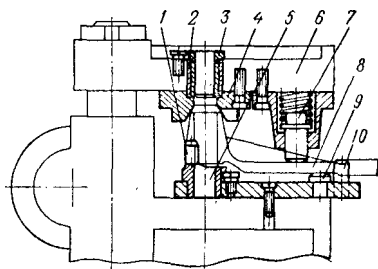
Наладка на скальчатый кондуктор для обработки отверстия в вилках
